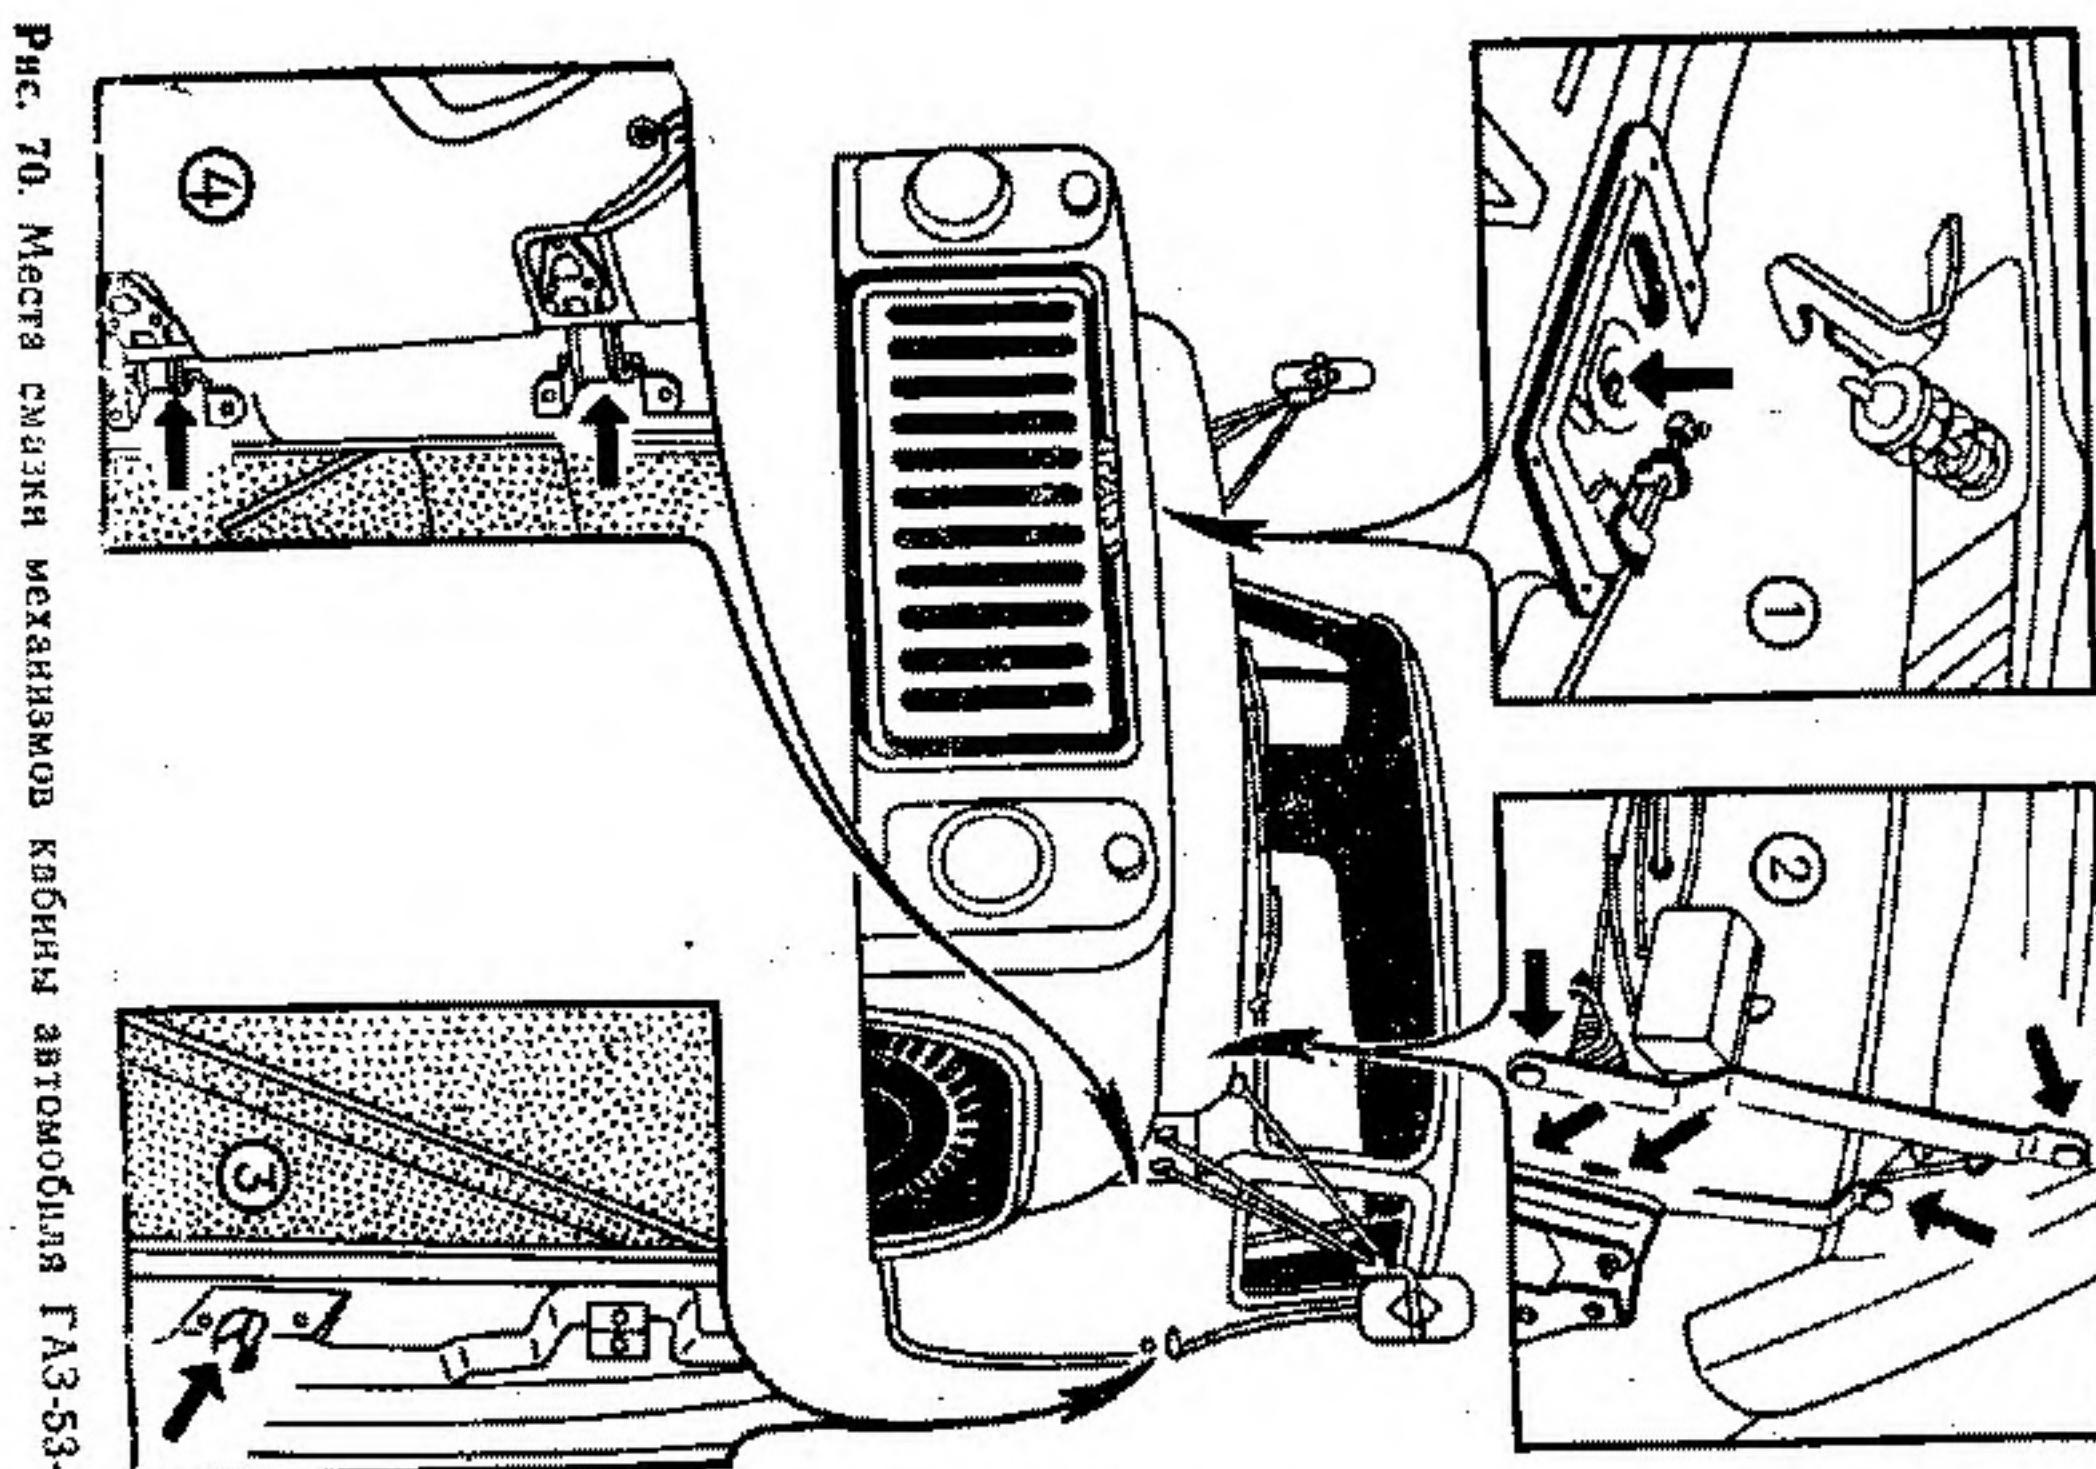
Места смазки механизмов кабины автомобиля ГАЗ-53-12
